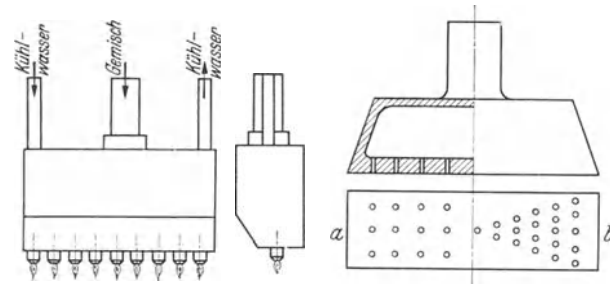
Wassergekühlter Düsenbrenner für Azetylen.
